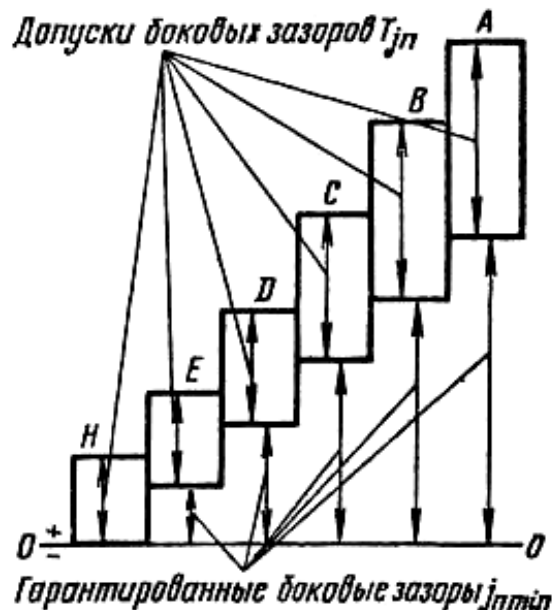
Схема расположения полей допусков боковых зазоров (T_{jn}) для принятых видов сопряжений зубьев зубчатых колес
